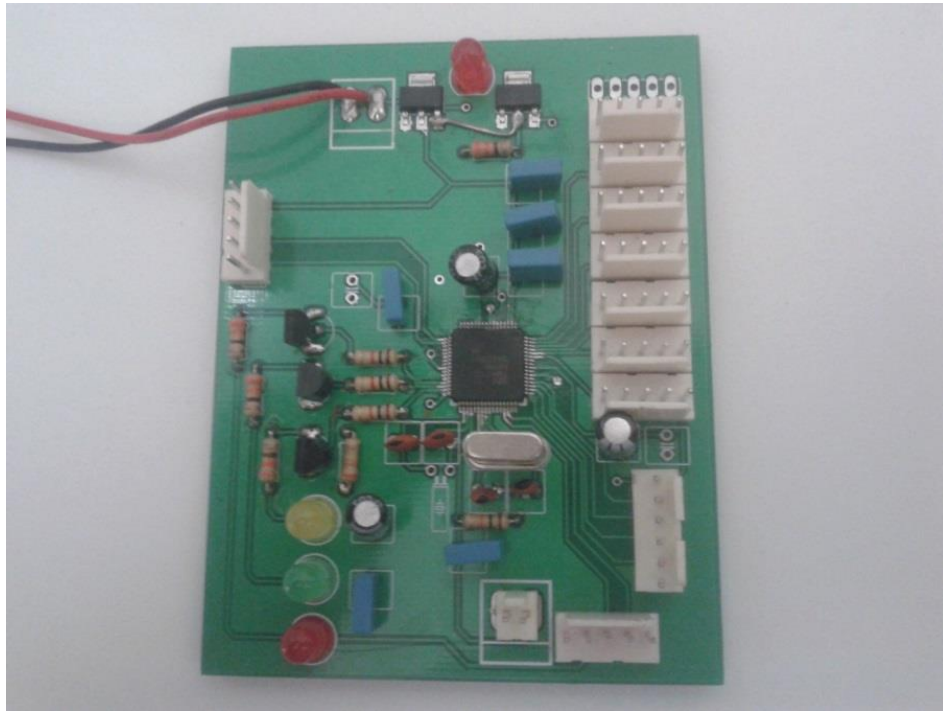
Foto da placa já com os componentes soldados.
